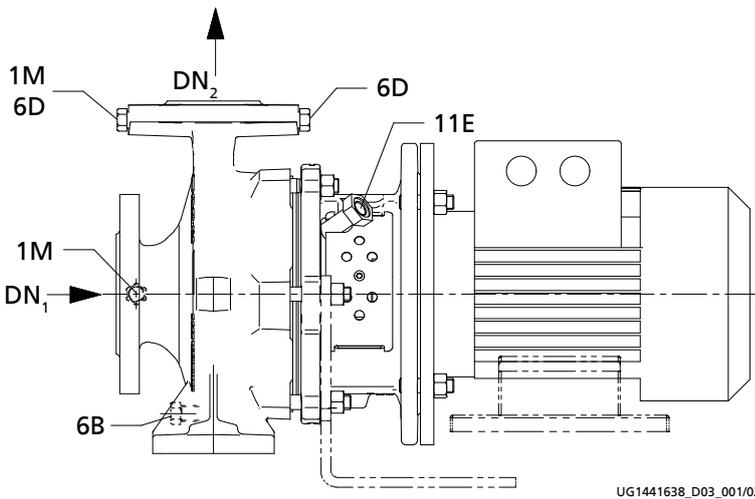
Cierre mecánico simple en tapa A con lavado externo (FA)
